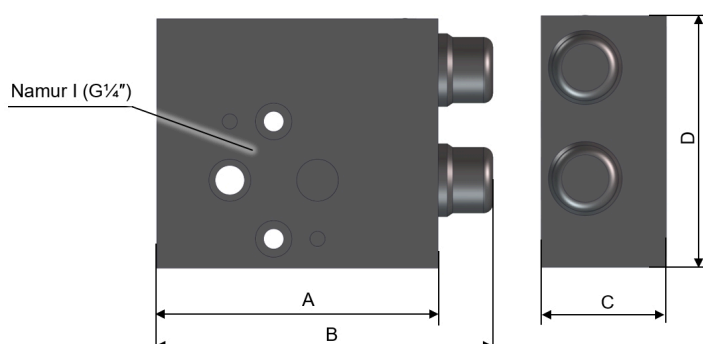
Dimensiuni principale bloc de accelerație cu efect simplu
